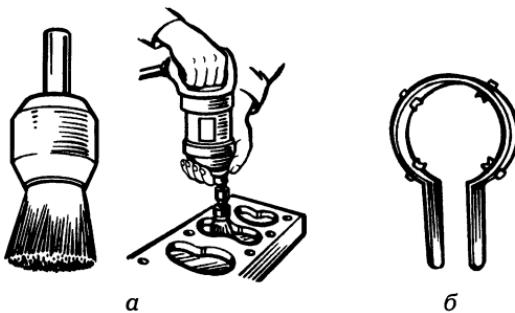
Приспособления для удаления нагара из головки цилиндров (а) и канавок поршней (б)
